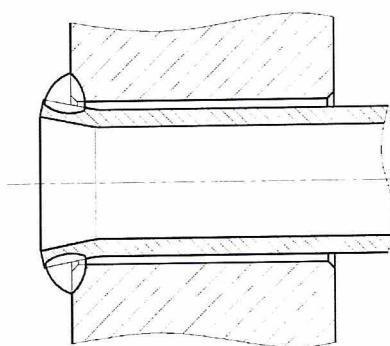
Сварка трубы с трубной решеткой
